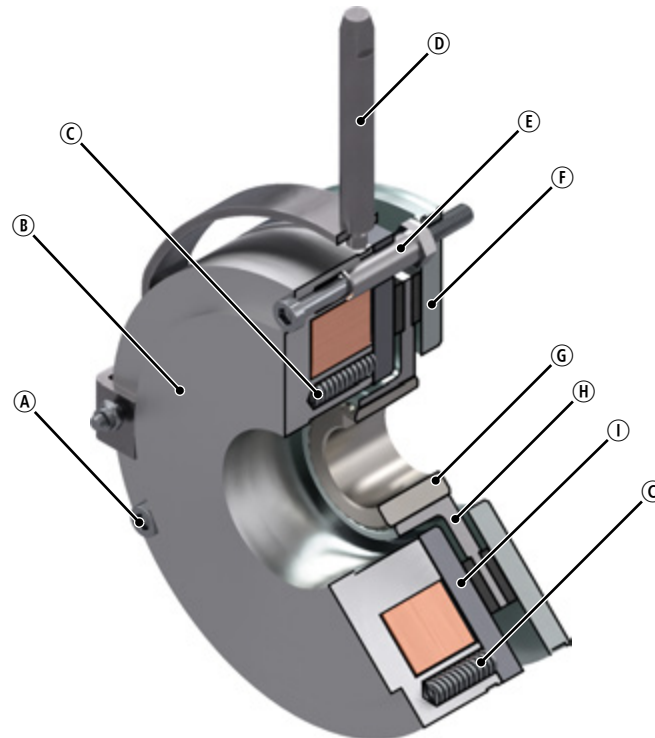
Aufbau einer Federkraftbremse INTORQ BFK458: Grundmodul N (Magnetteil komplett) + Rotor + Nabe + Flansch / Reibblech
